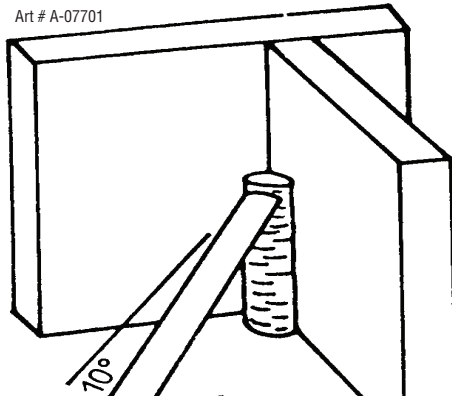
Soldadura de perfil en ángulo vertical de un solo recorrido
